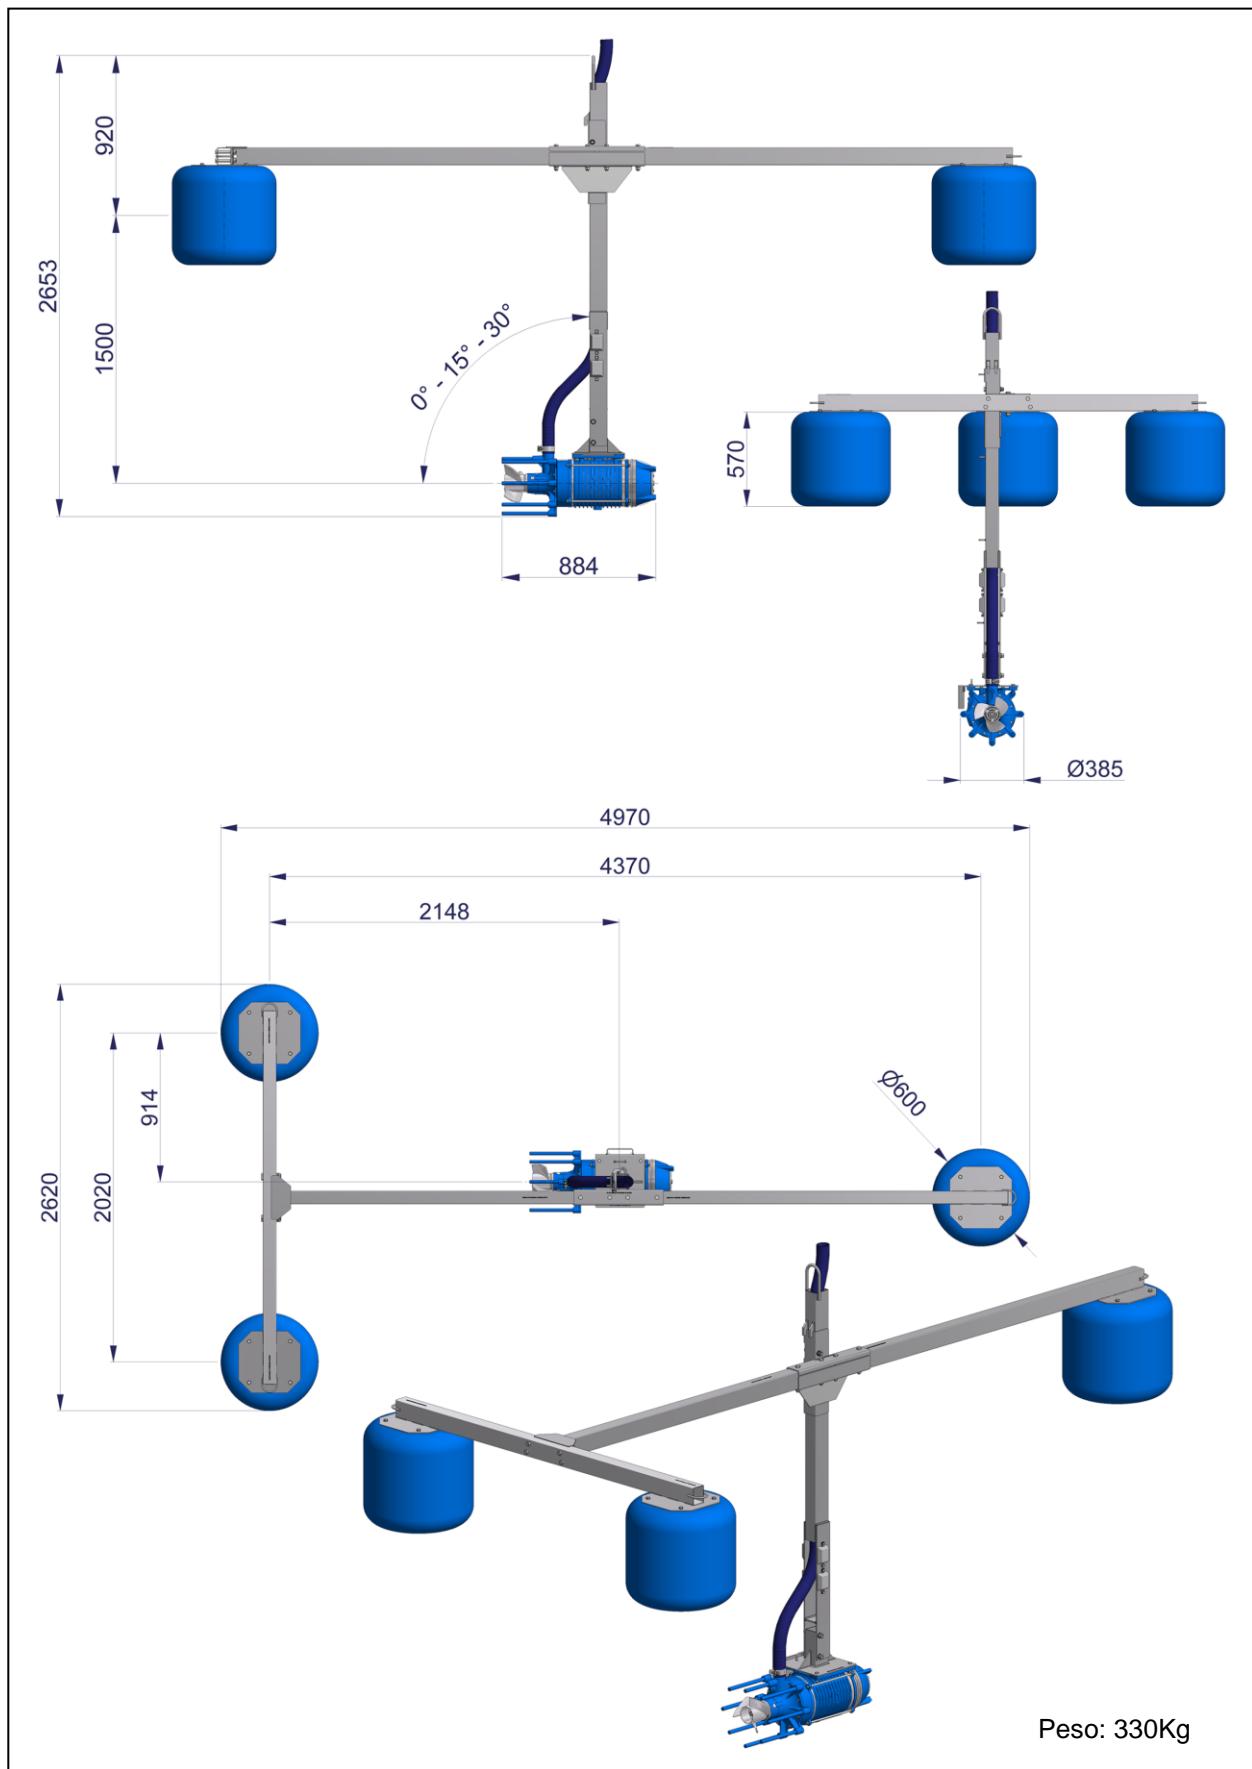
Dimensional TORNADO 25, 30 e 40CV
